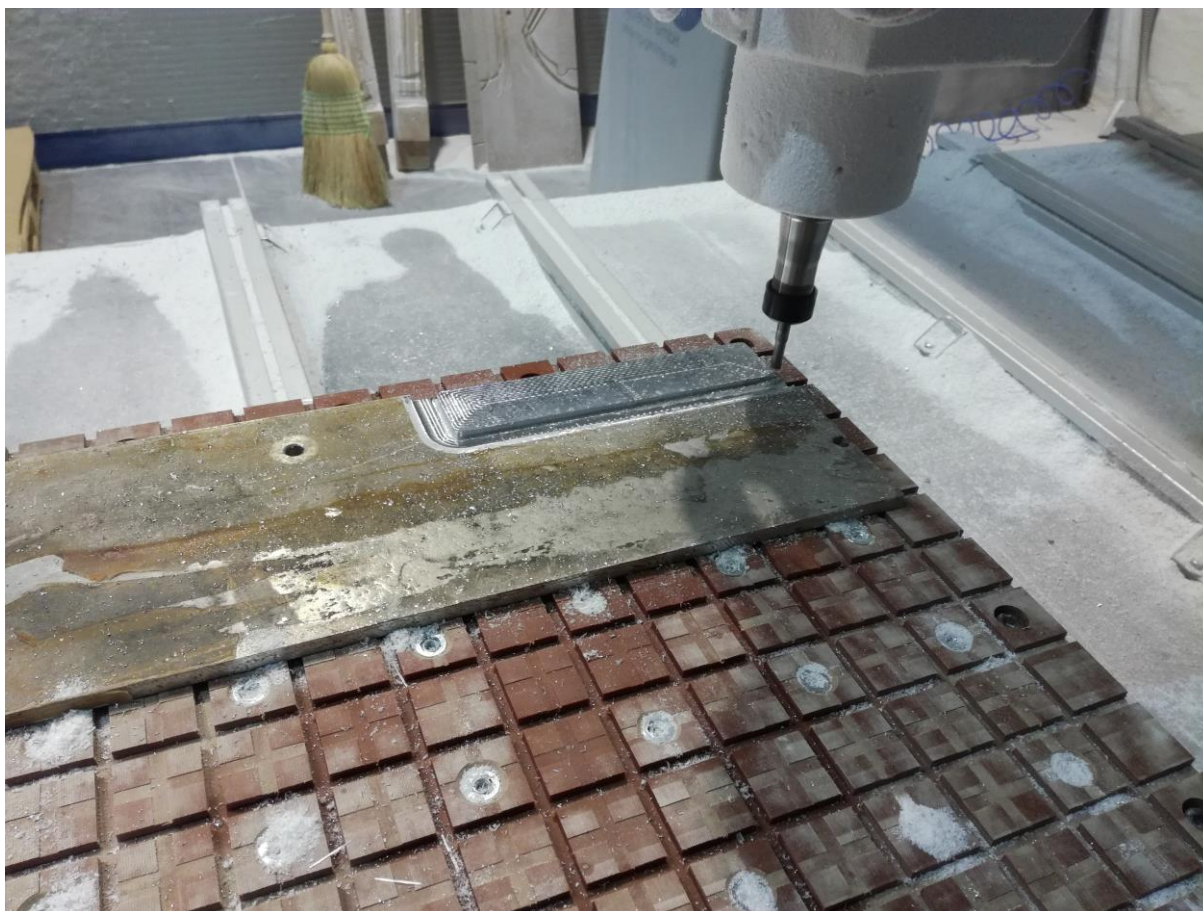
Prenosivi vakuum stol stegnut za aluminijski stol
